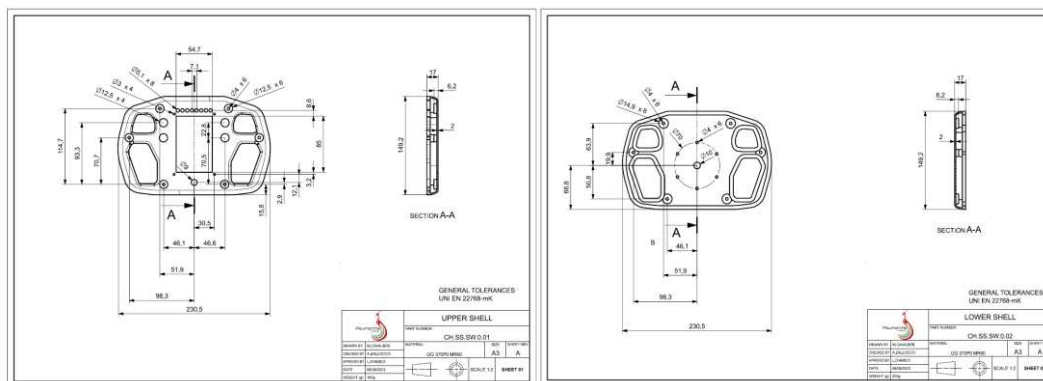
guscio del volante, disegno tecnico, parti superiore ed inferiore
